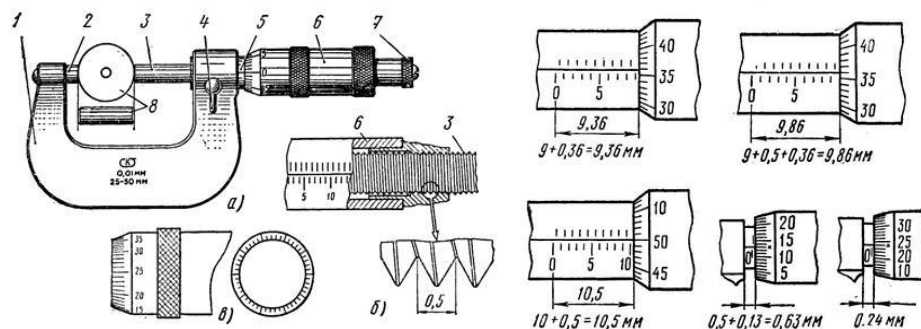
Микрометр гладкий. а – устройство; б – микрометрический винт; в – барабан; 1 – скоба; 2 – пятка; 3 – винт; 4 – стопор; 5 – стебель; 6 – барабан; 7 – трещотка; 8 – установочные меры
